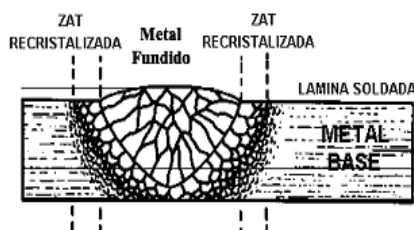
Esquema de las zonas involucradas en un cordón de soldadura. Fuente: Marulanda *et al.* (2007).
